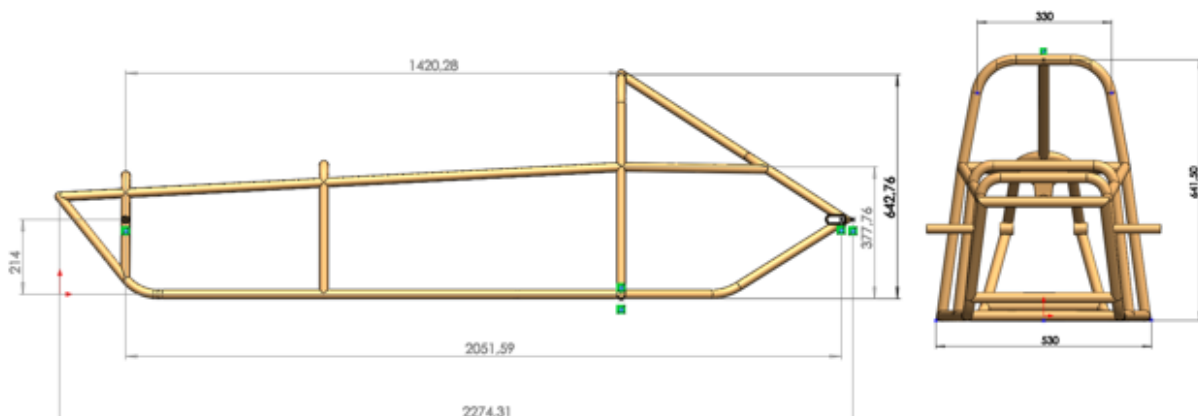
Dimensões gerais do chassi definitivo em milímetros
